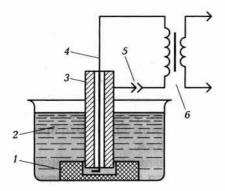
Установка для прошивки неметаллов электрогидравлическим способом:
